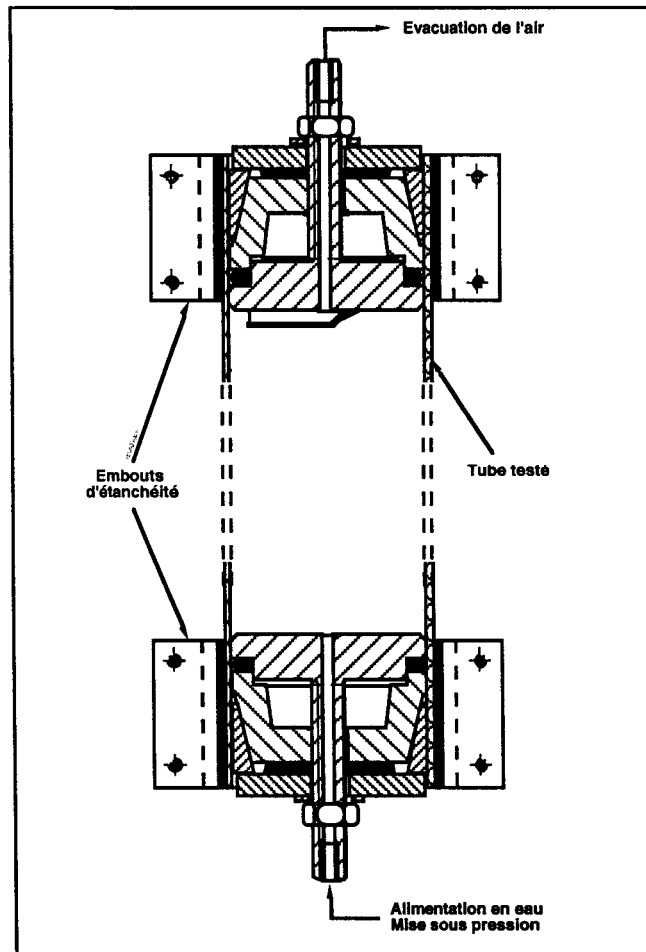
Tube équipé de ses bouchons - Vue en coupe
